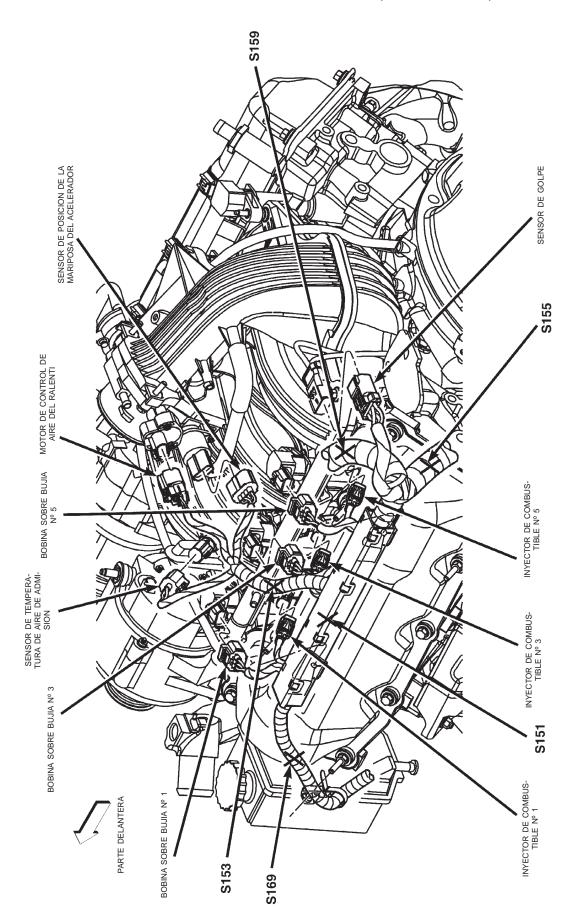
LADO IZQUIERDO DEL MOTOR 3.7L
